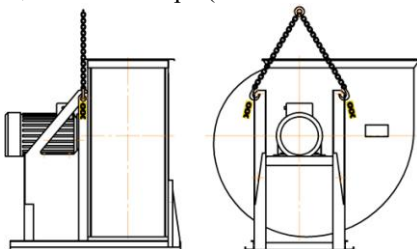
Схема строповки центробежных вентиляторов 1-й конструктивной схемы.
